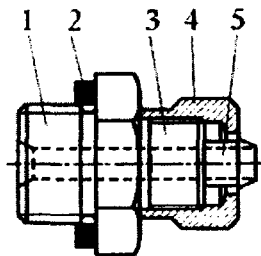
Устройство для ниппельного-резьбового соединения шланга:
